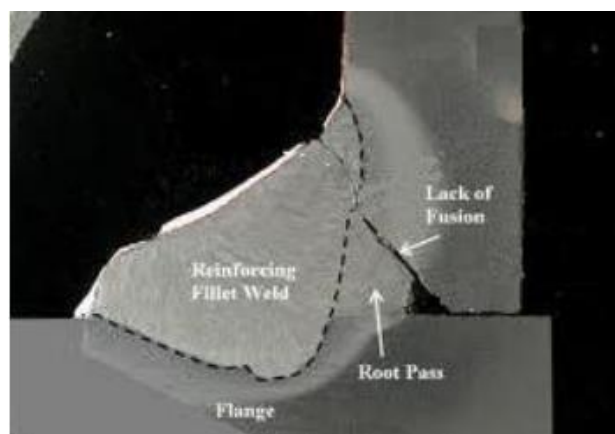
Manque de fusion à la racine de la soudure
